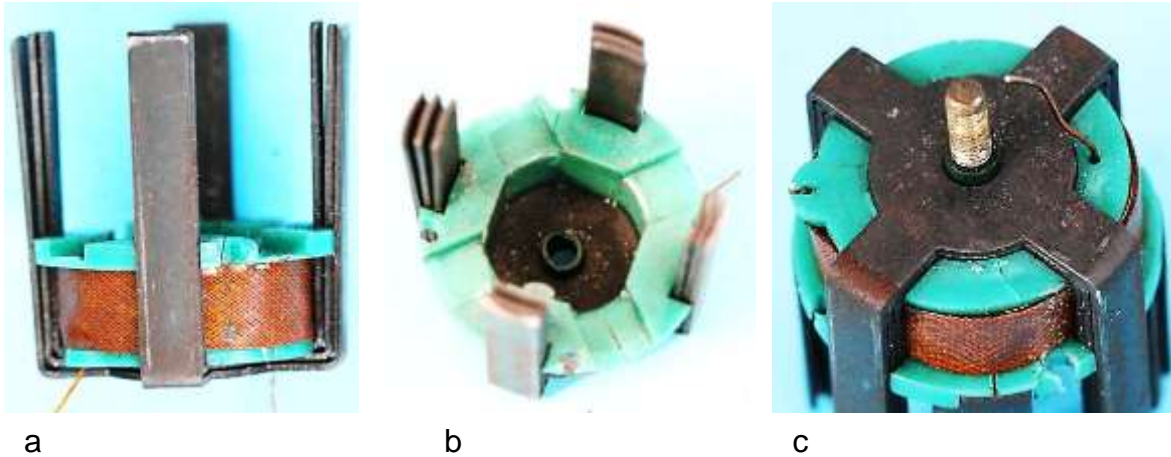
Unterer Klauenpolring: a) Länge Klauenpolle, b) Spule mit Durchführung für den Kabelanschlussbolzen, c) Joch mit den abgewinkelten Polen
